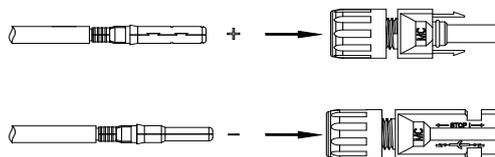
Assemblaggio dei cavi positivo e negativo
